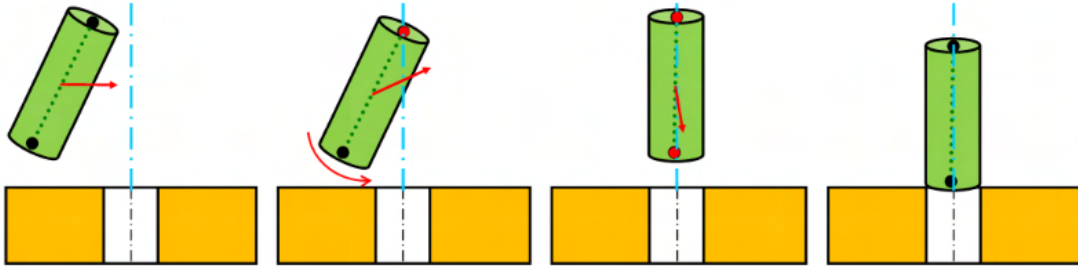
Illustration du guidage géométrique, vue en 2D, pour l'assemblage *peg-in-hole*.
